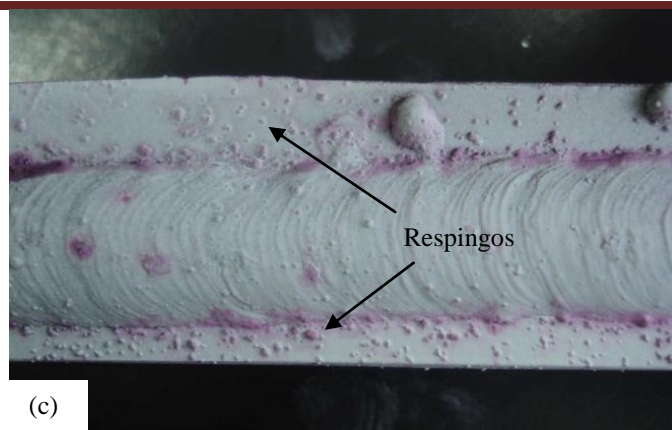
Cordão de solda após inspeção por líquidos penetrantes. (a) Cav17Ar, (b) Cav19Ar, (c) Cav22Ar
